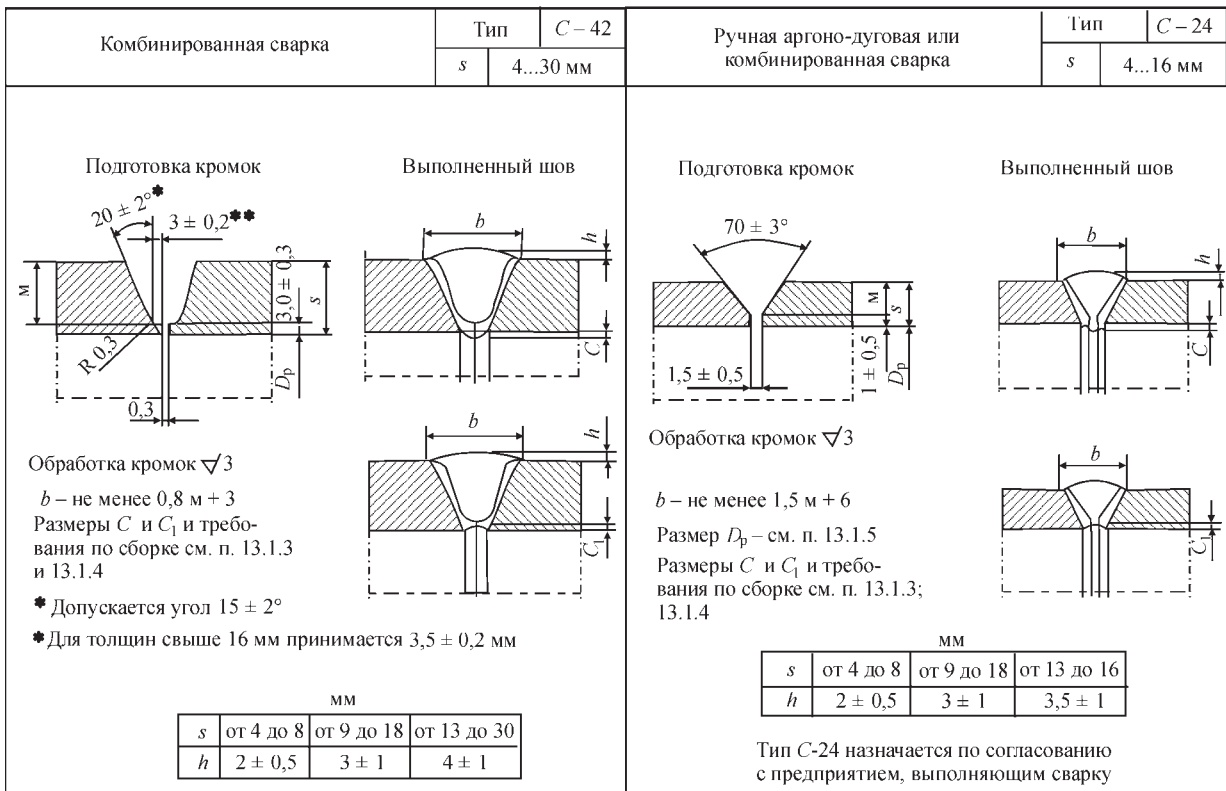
Конструкции сварных соединений трубопроводов Ду-300 в соответствии с рекомендациями ОП 1513-72 и ПНАЭГ-7-09-89
